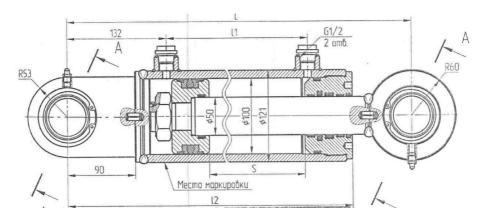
Гидроцилиндры прессующего механизма
